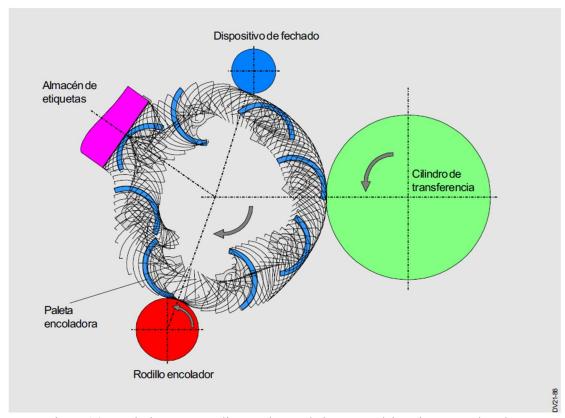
Movimiento que realizan cada una de las partes del conjunto y cada paleta
